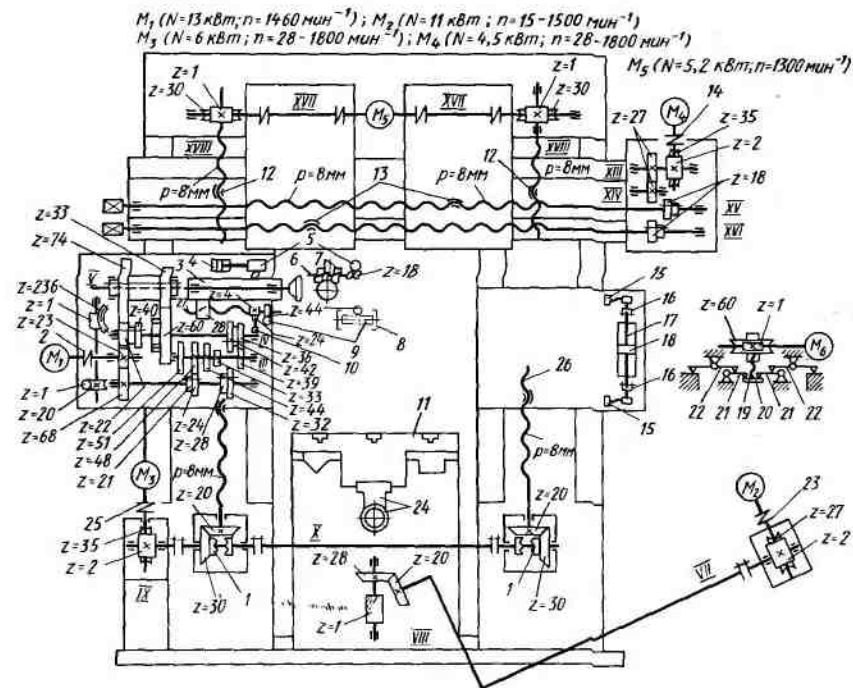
Кинематическая схема продольно-фрезерного станка мод. 6610
